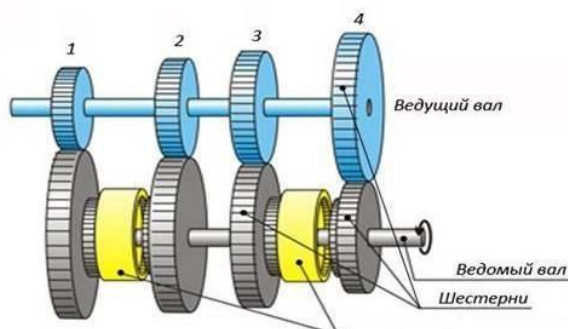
Схемаредуктора-коробки передач с механической передачей
